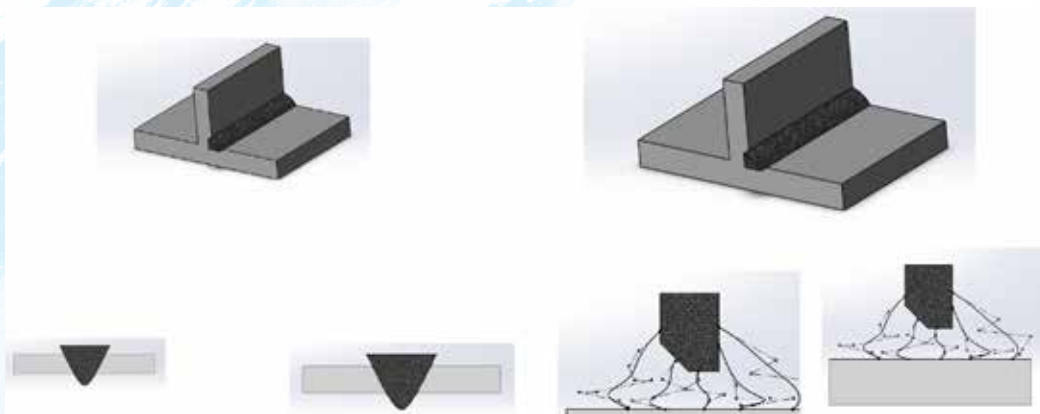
Tipo de grietas en uniones a tope y en T
